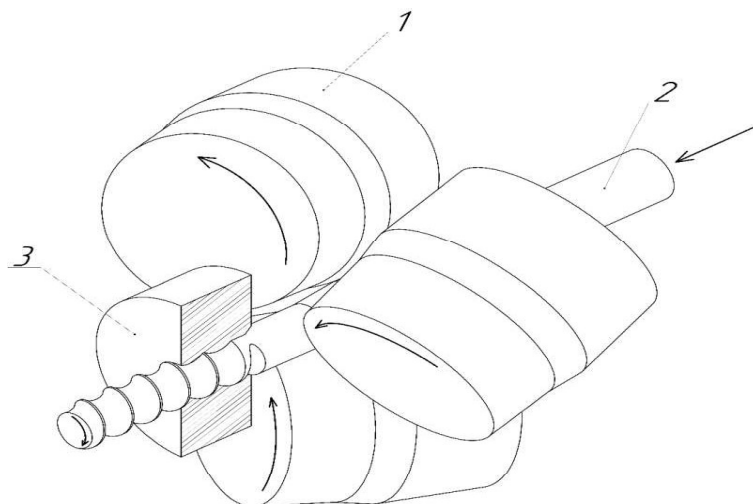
Совмещенный способ получения арматурного профиля: 1 – прокатные валки, 2 – заготовка, 3 – матрица
